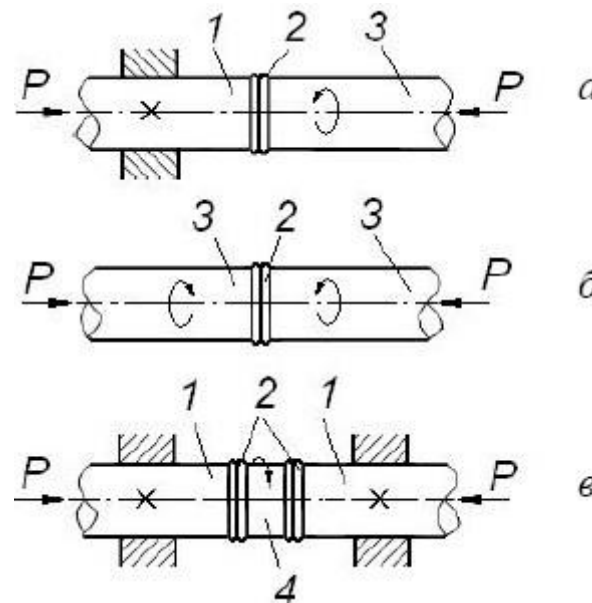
Схемы сварки трением с использованием вращения одной детали (а), обеих деталей (б) и вставки (в): 1 – неподвижная деталь; 2 – сварной шов; 3 – вращающаяся деталь; 4 – вставка
